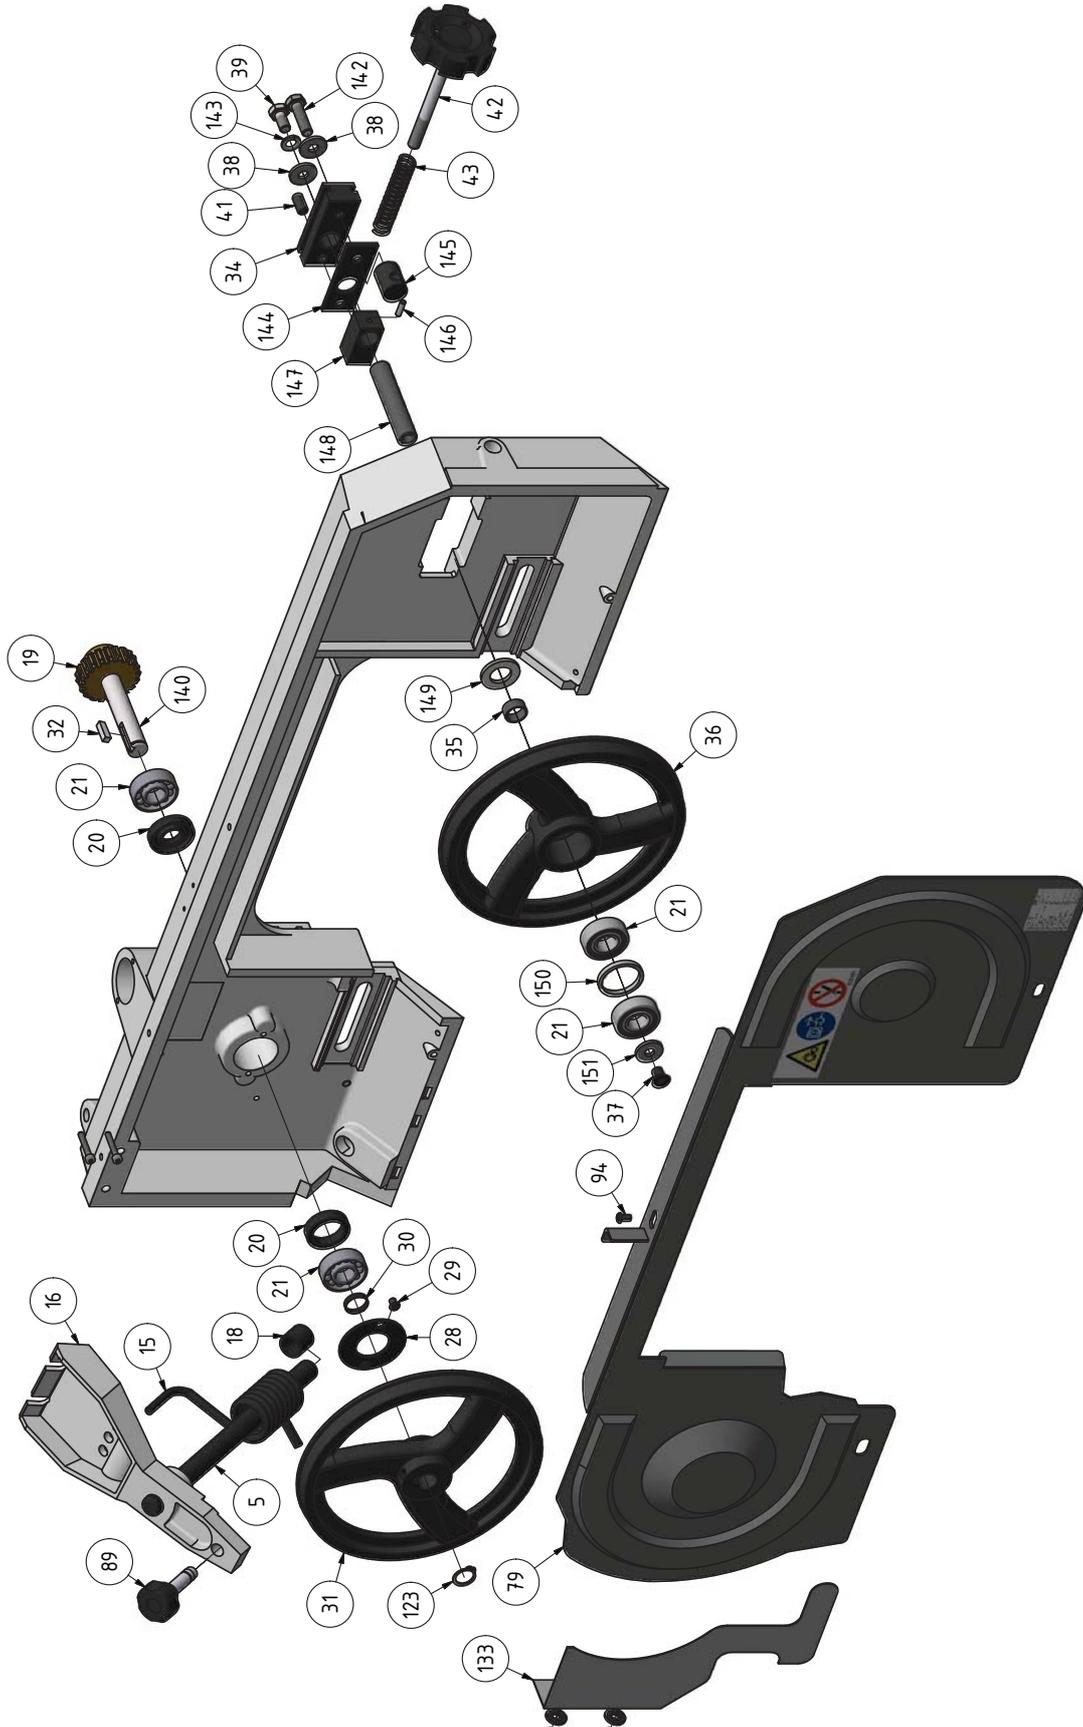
Ersatzteilzeichnung 2 von 4 - Parts drawing 2 of 4
